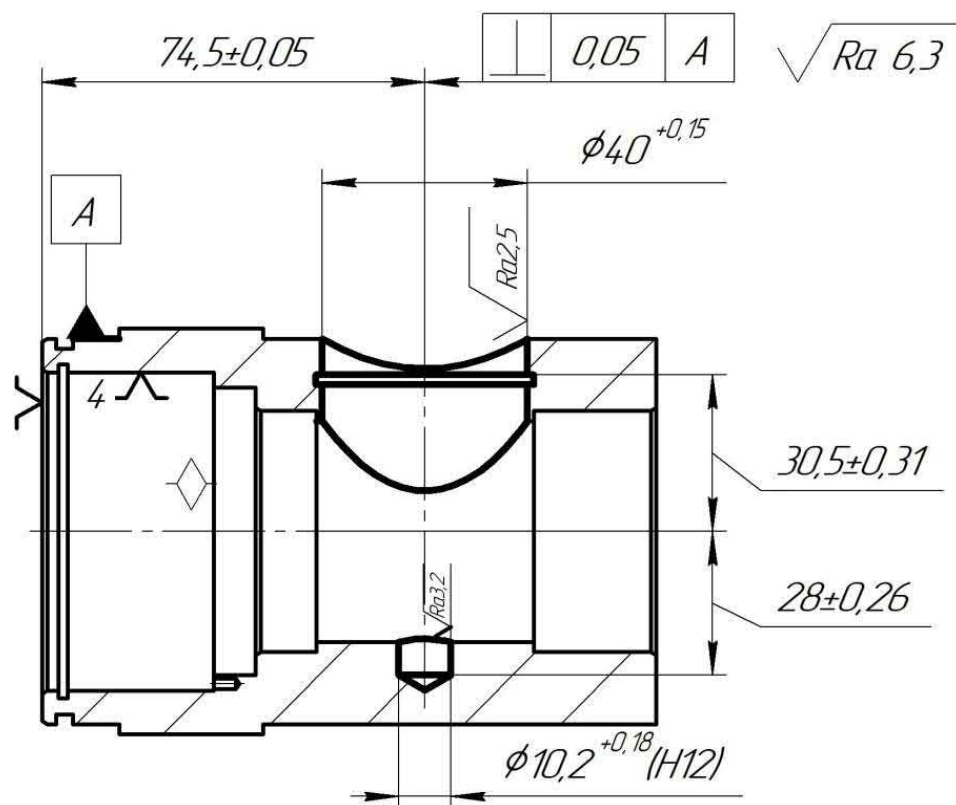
эскиз для фрезерной операции с ЧПУ 055
